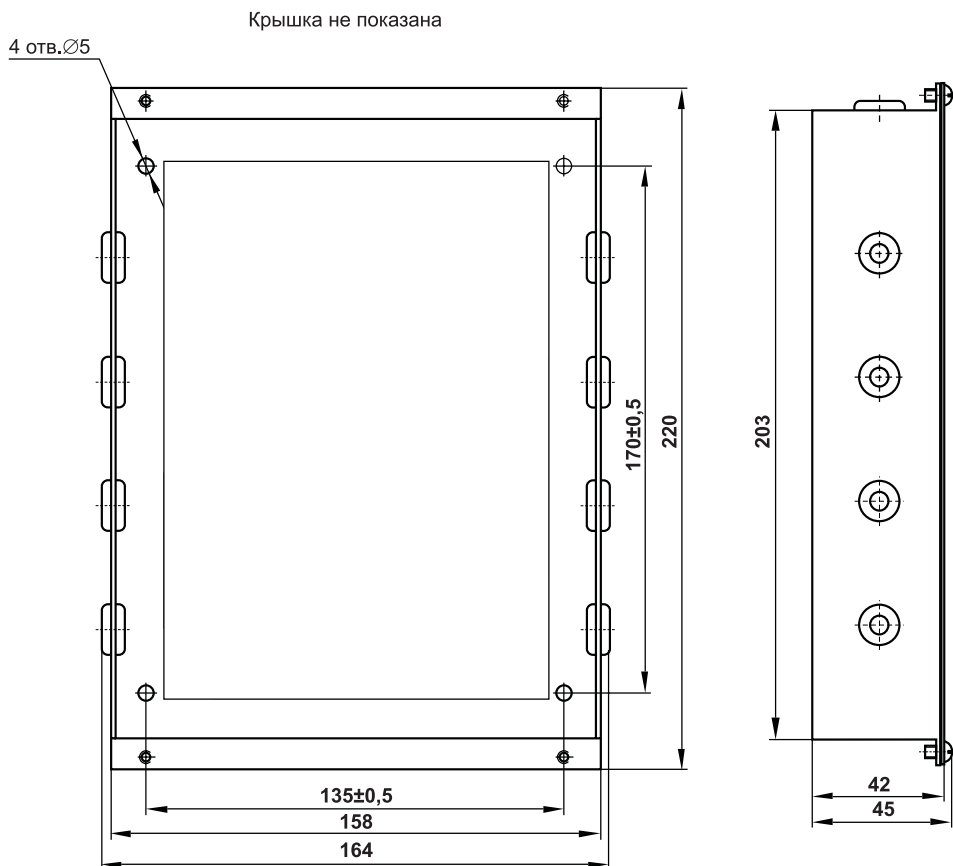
Габаритный чертеж адаптер блока вызова PERCo-DA-01.
